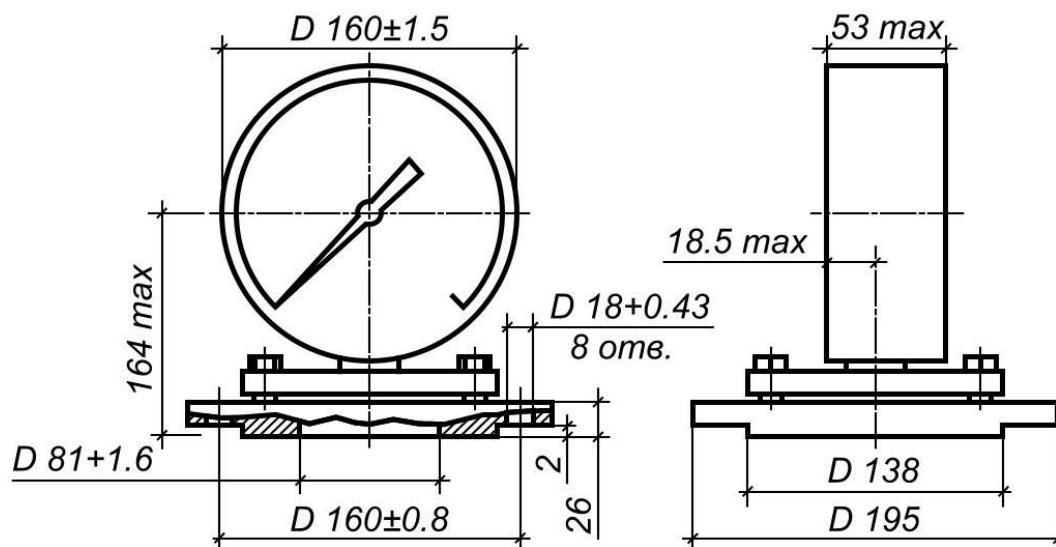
Габаритные и присоединительные размеры приборов исполнения 2
